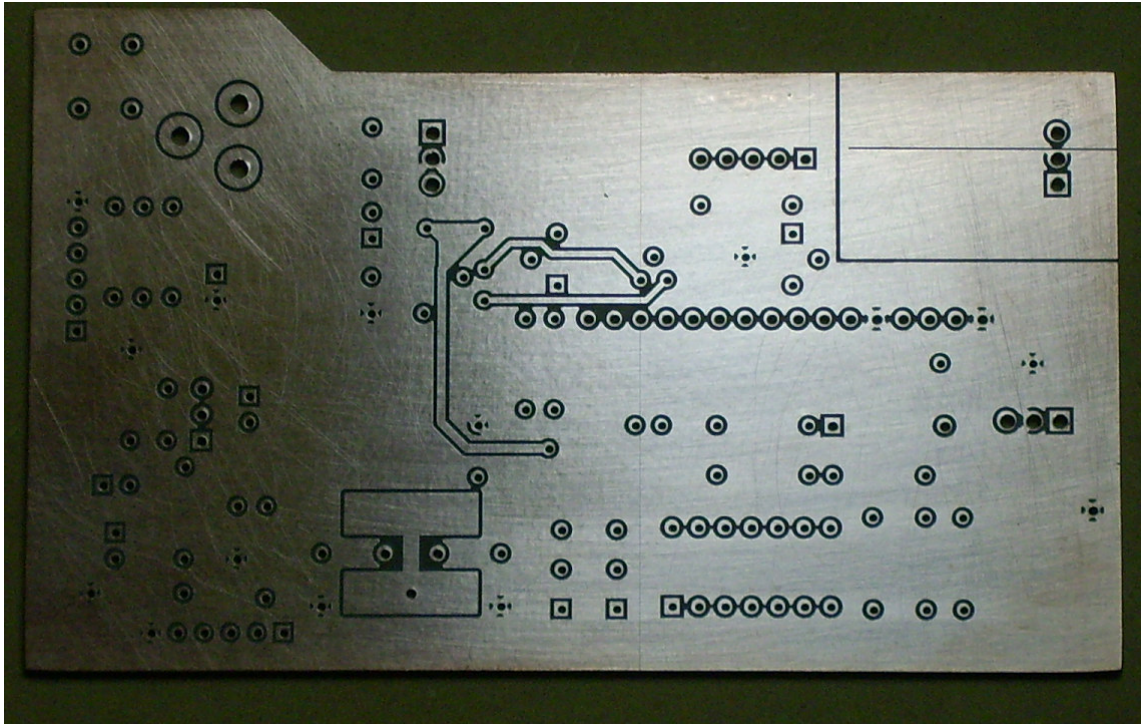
Face superior da placa de circuito impresso do Módulo Móvel
